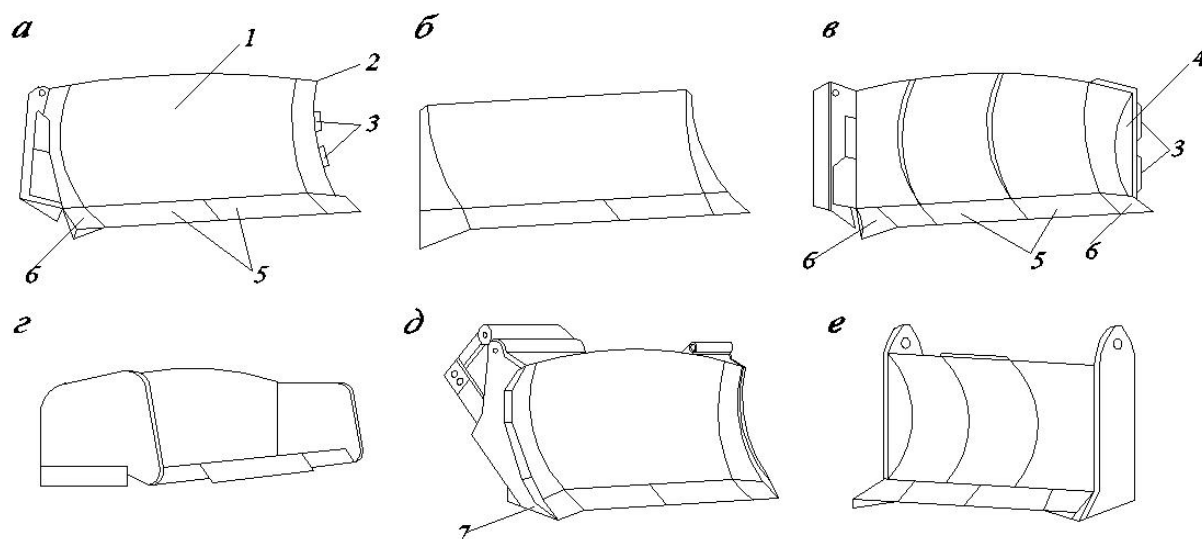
Основные типы отвалов бульдозера: *а* – прямой; *б* – поворотный; *в* – сферический; *г* – совковый; *д* – с боковыми рыхлящими зубьями; *е* – короткий толкающий; 1 – лобовой лист; 2 – боковые щитки; 3 – боковые ножи; 4 – открьлки; 5 – ленточный средние ножи; 6 – угловые ножи; 7 – выдвижные зубья
